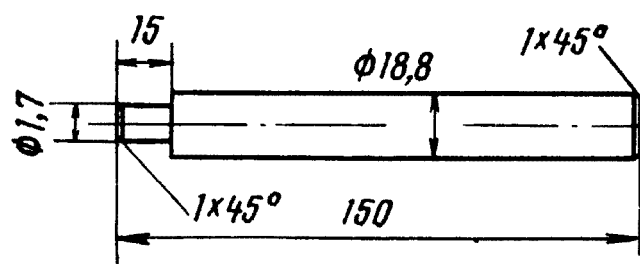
Оправка для выпрессовки и запрессовки подшипников в опору корпуса насоса рулевого управления
